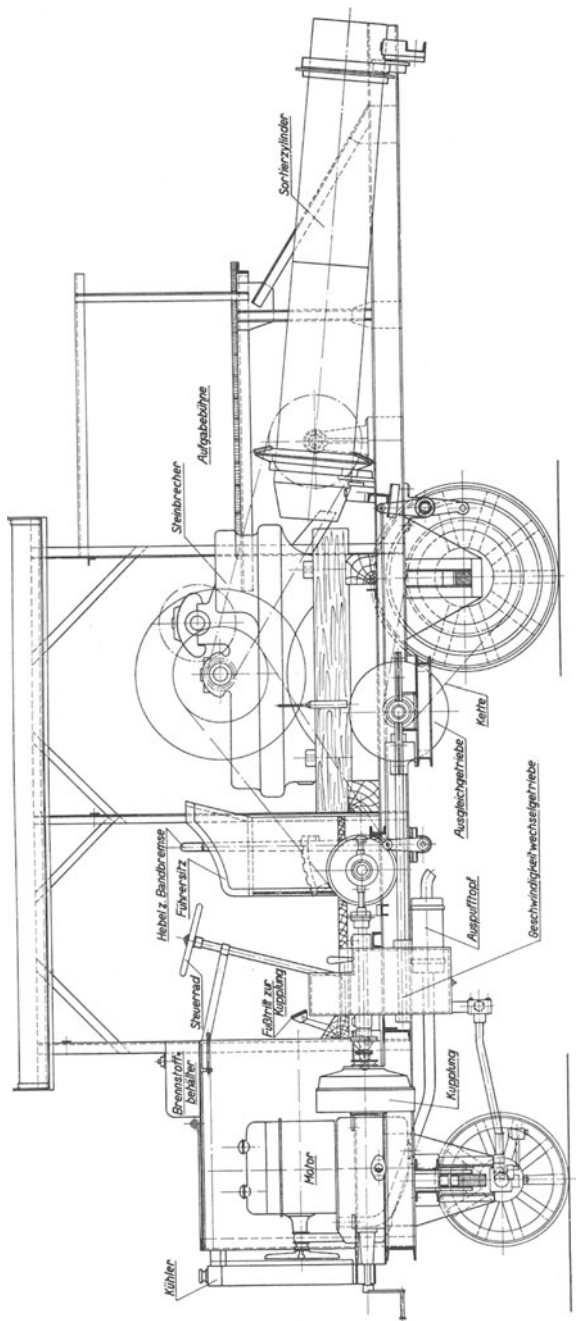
Fahrbare Schotter- und Siebanlage der Maschinenfabrik M. Friedrichs & Co.
